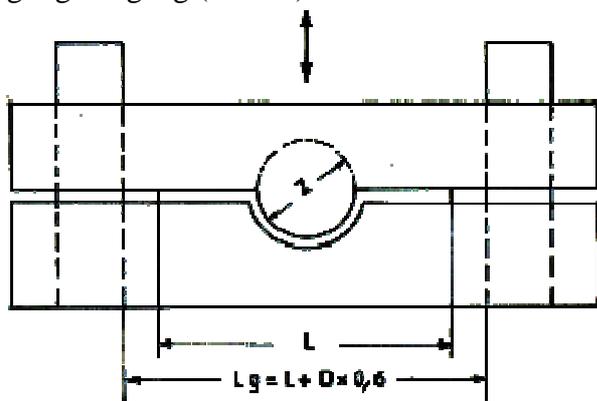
Formwerkzeug für Schildzapfengurt ( $Z = \text{Zapfendurchmesser}$ ).
